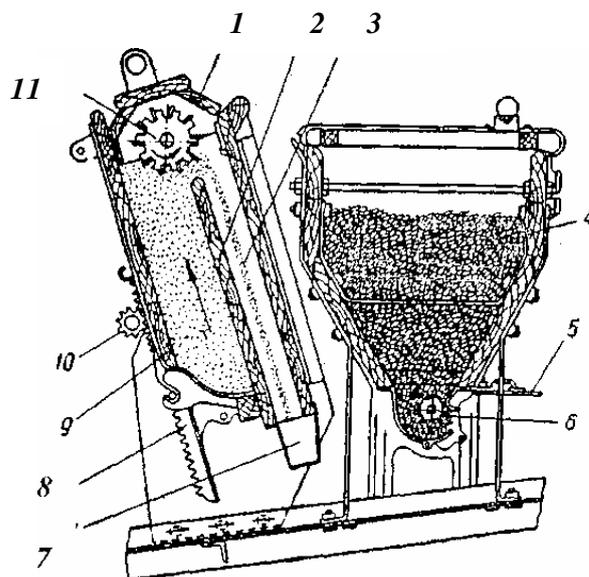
Схема розташування ящиків комбінованої сівалки з барабанно-фрезеруючим туковисівним апаратом конструкції "Schleera":
